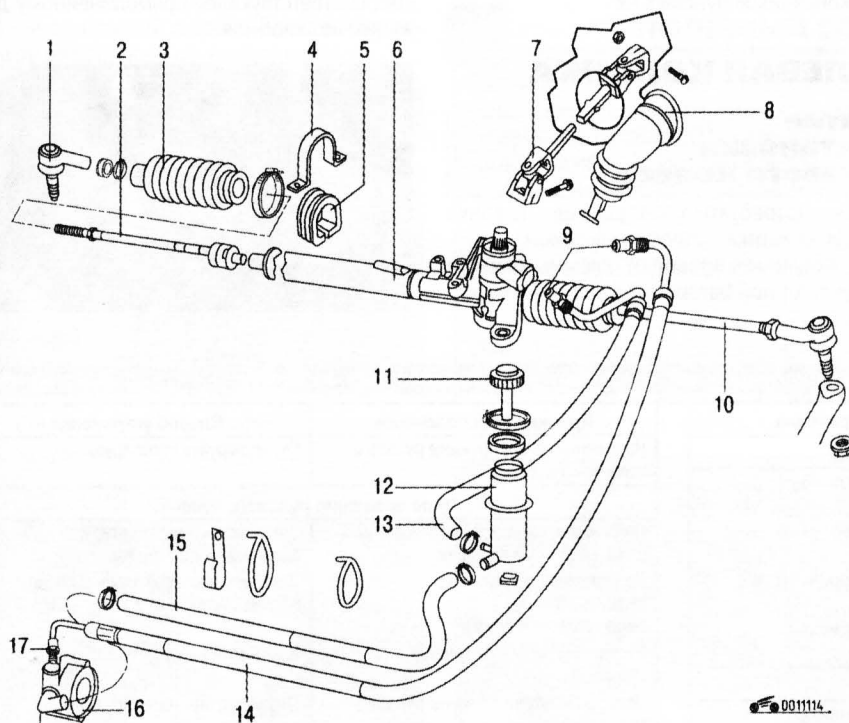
Рулевой механизм с гидроусилителем: 1 – наконечник рулевой тяги; 2 – правая рулевая тяга; 3 – защитный кожух; 4 – скоба крепления; 5 – резиновая подушка; 6 – рулевой механизм; 7 – промежуточный вал с универсальными шарнирами; 8 – защитный кожух; 9 – уплотнительное кольцо; 10 – левая рулевая тяга; 11 – пробка с указателем уровня; 12 – бачок; 13 – возвратный шланг; 14 – напорный шланг; 15 – всасывающий шланг; 16 – насос; 17 – штуцер с уплотнительным кольцом
